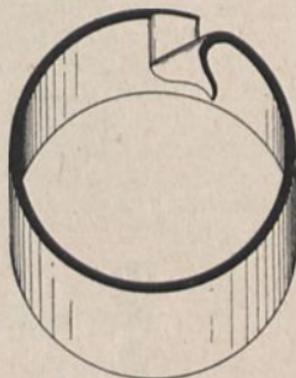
70/76 mm-Patentrohr mit schlechter Schweißung. Federzeichnung nach der Natur. Der abgegebene Lappen ist nachträglich durch den Monteur umgeschlagen. Am Rohr selbst ist kein Schweißfehler zu erkennen.
